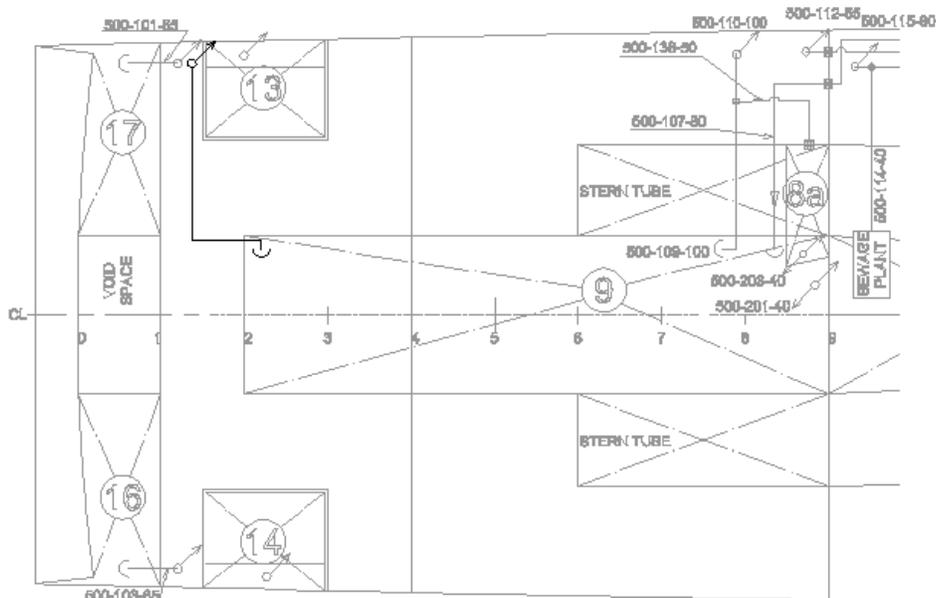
Vue en plan de la disposition de la ventilation proposée
